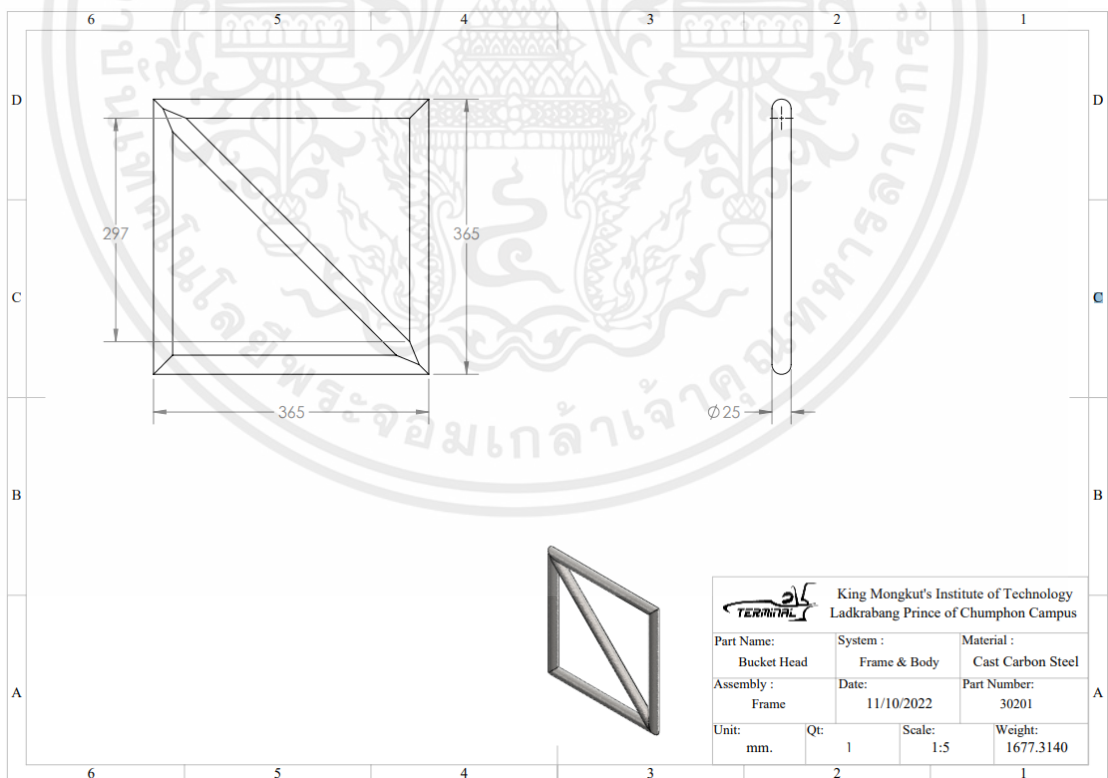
โครงรถด้านหน้า (Bucket Head to Front Hoop)
